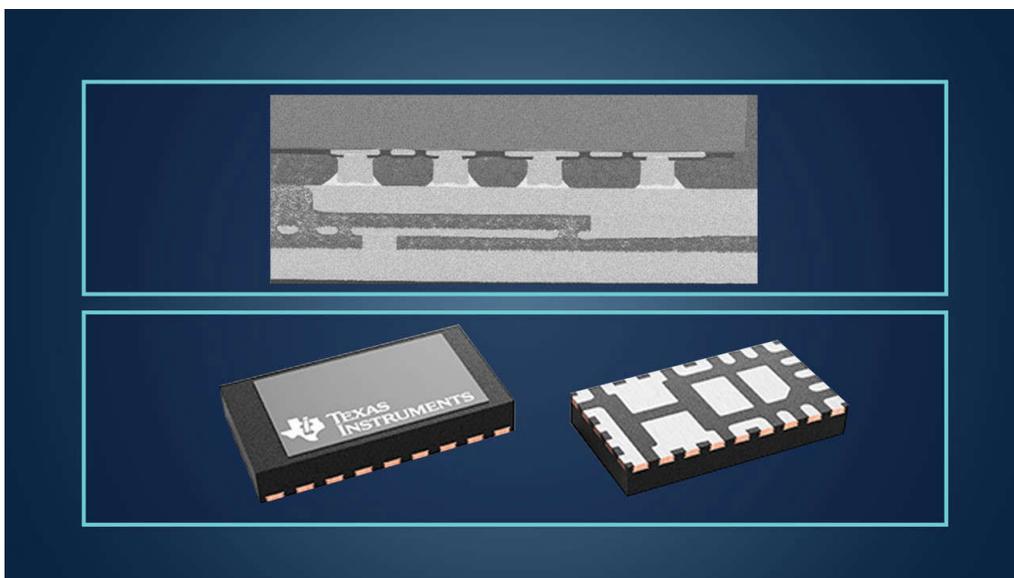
增強型 HotRod 技術可將矽晶連接至厚銅佈線層。此方法可實現極低的 PCB 電阻，同時提供導熱片或符合標準化封裝尺寸的靈活性。
